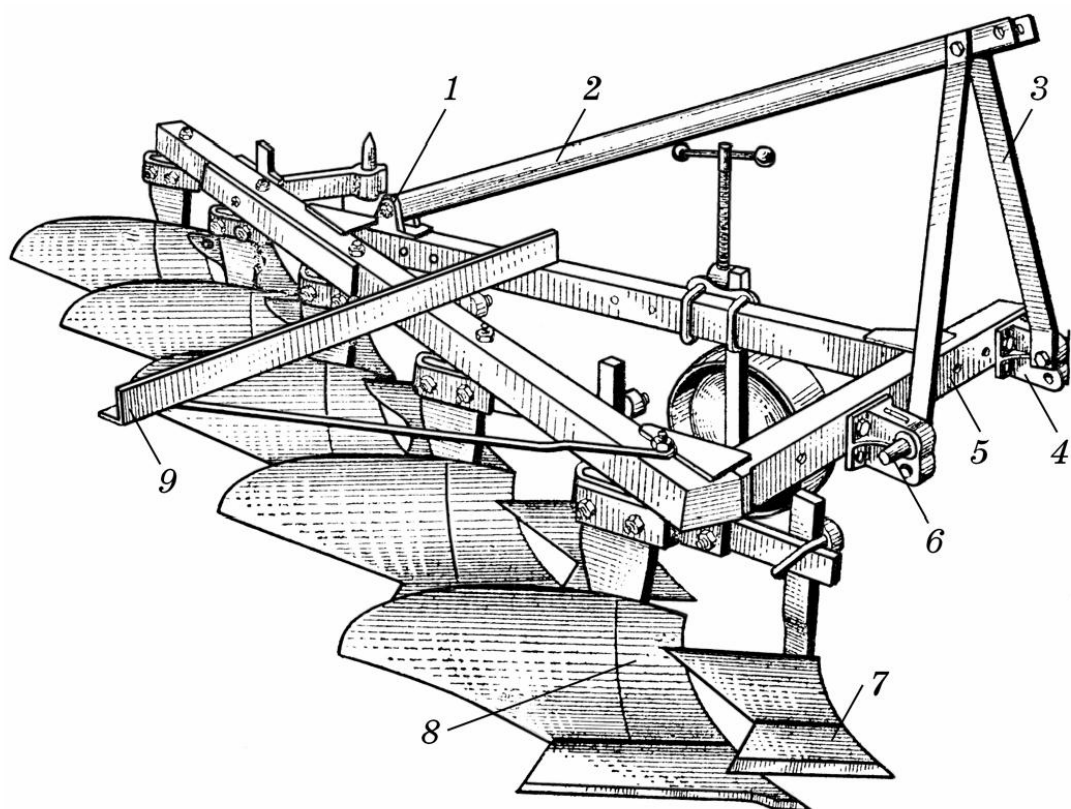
Плуг п'ятикорпусний начіпний ПЛН-5-35:
